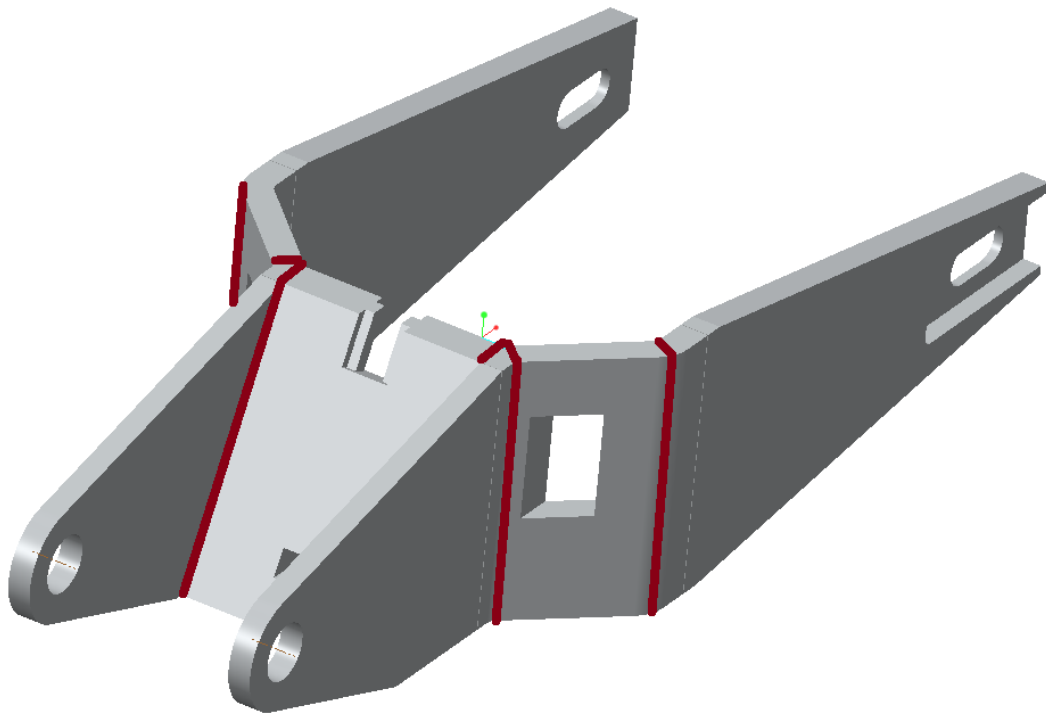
Basculante soldado. Líneas granates: Zonas supuestamente soldadas.
